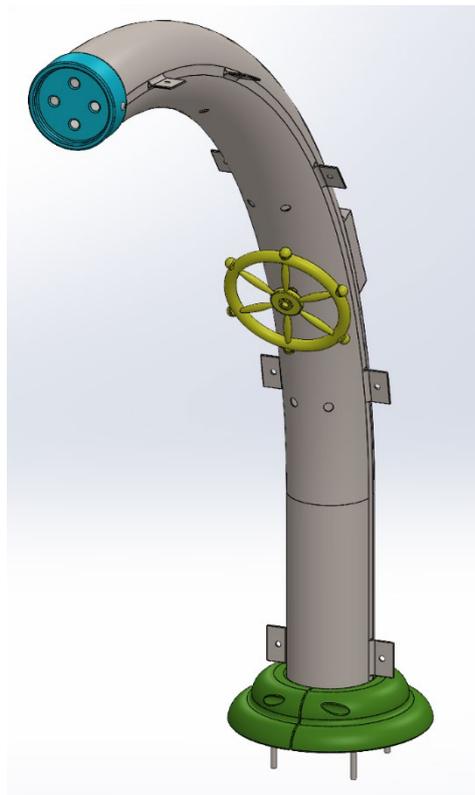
Ensamblaje tubo con accionamiento de rueda.
